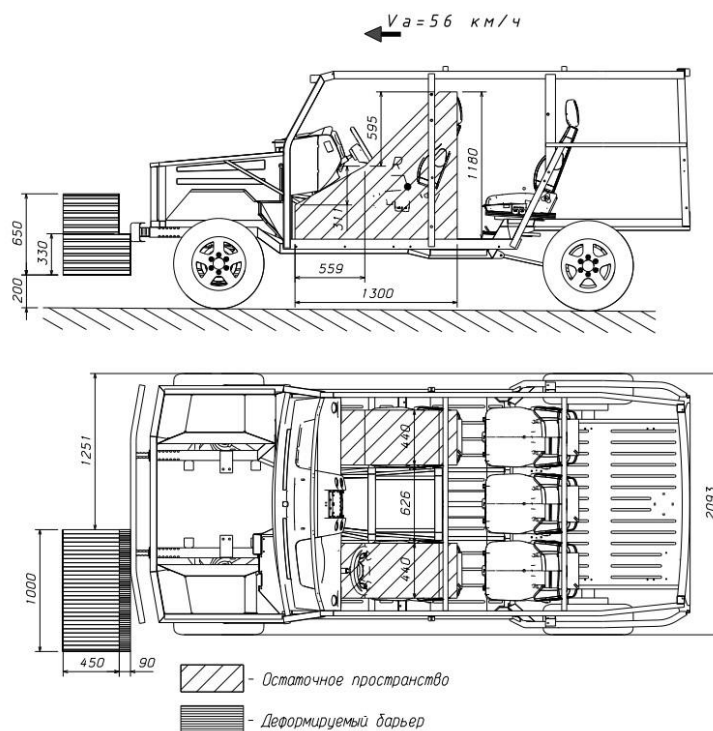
Схемы столкновения модели с барьером (вид сбоку и сверху)
